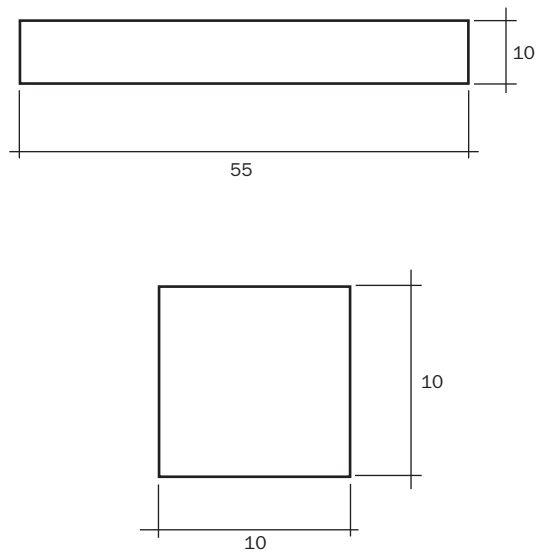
Dimensional do corpo de prova sem entalhe – ensaio Charpy
